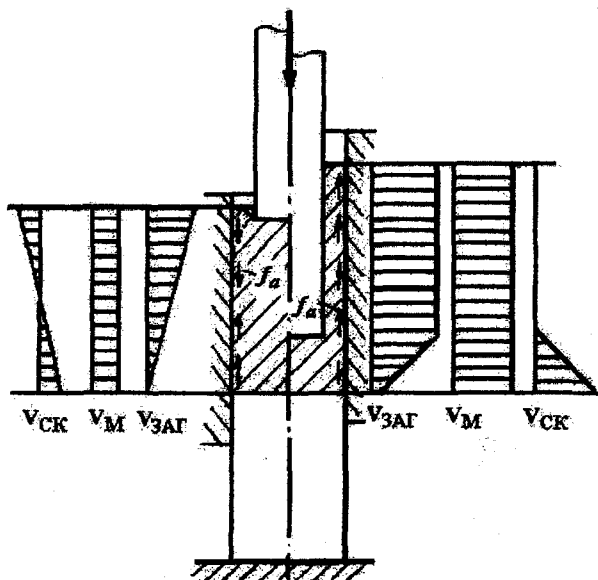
Выдавливание с активными силами трения стаканов из спеченных порошковых заготовок
